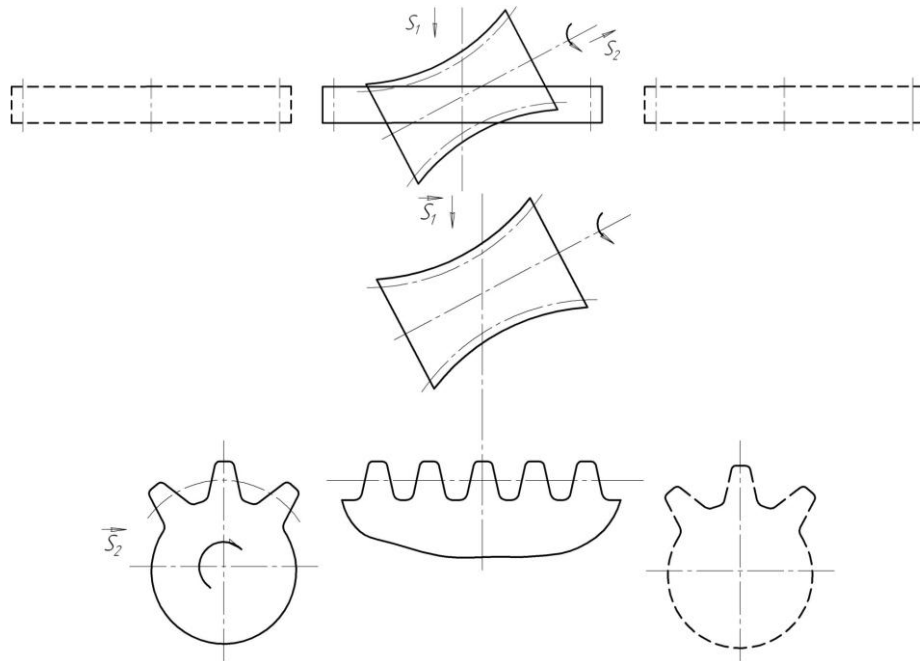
Схема нарізування витків гіперболоїдного інструменту
